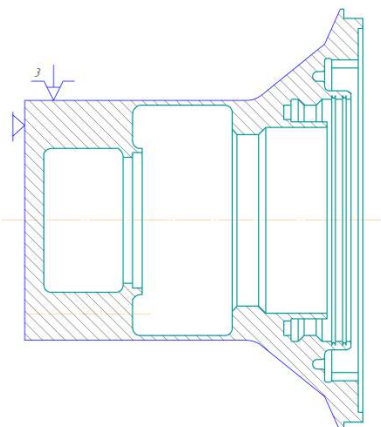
Схема базирования заготовки на комплексной операции с ЧПУ (установ 1)
